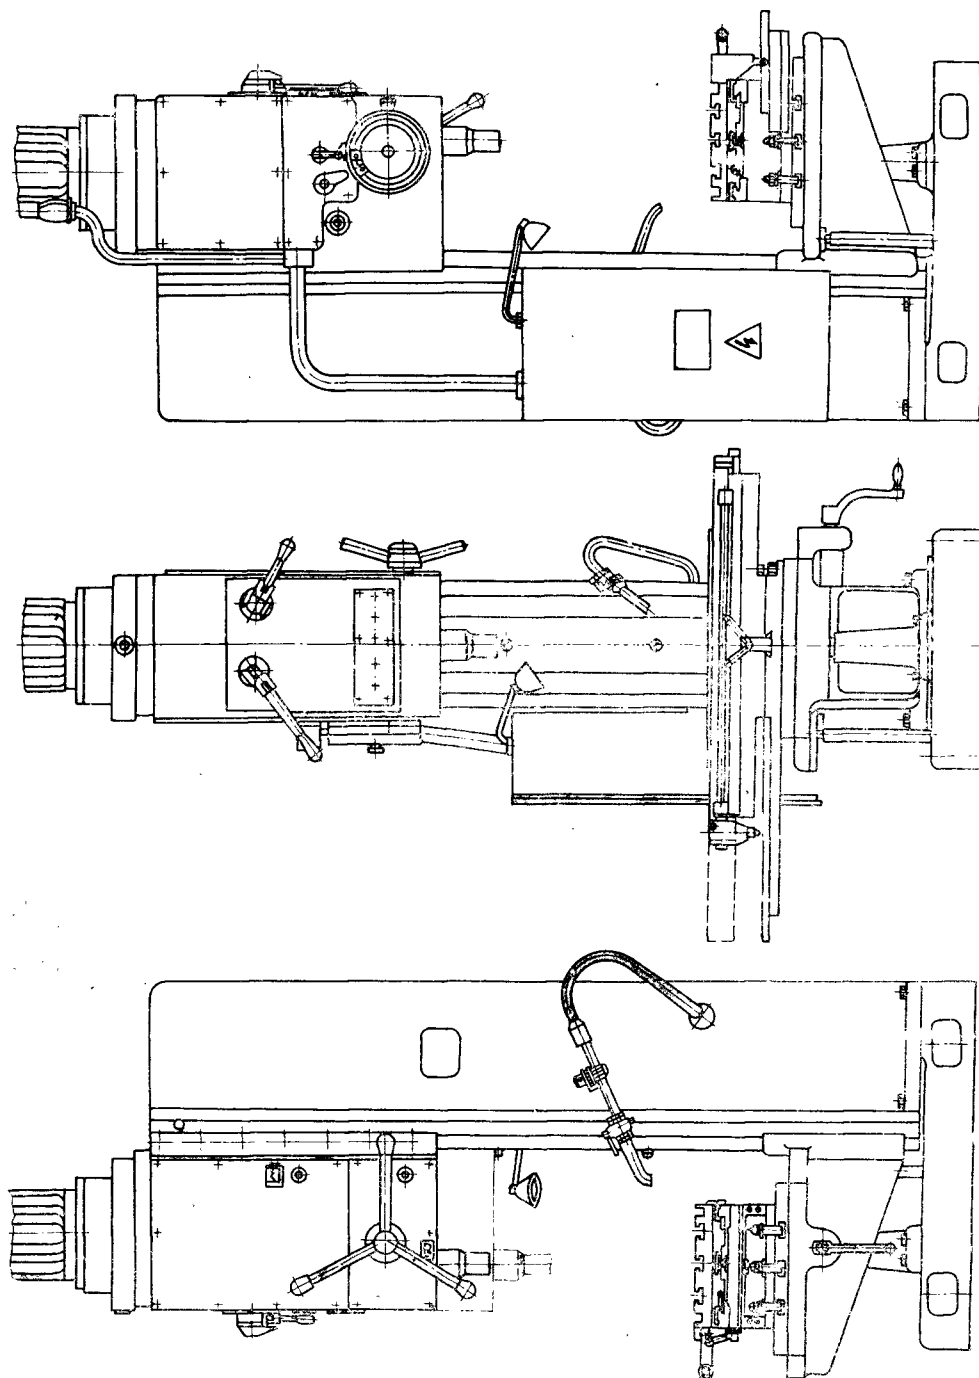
ОБЩИЙ ВИД станка 2С132К
